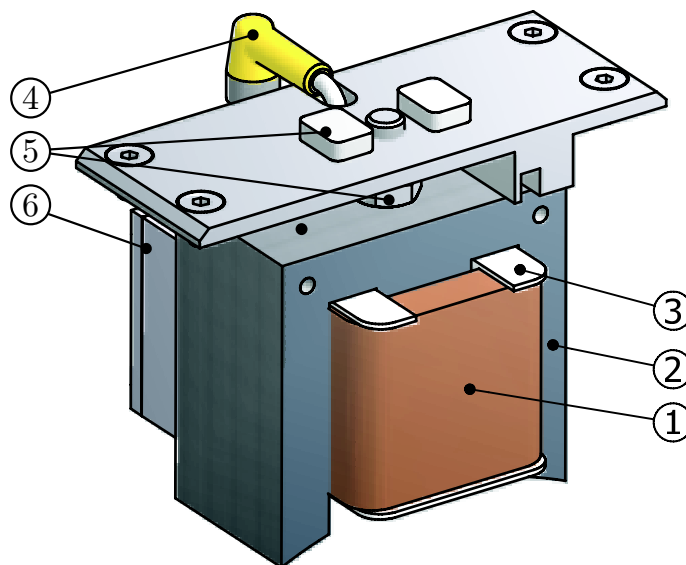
3D-Ansicht eines Elektromagneten sowie Montageplatte und Stecker des Wirbelstromsensors:
